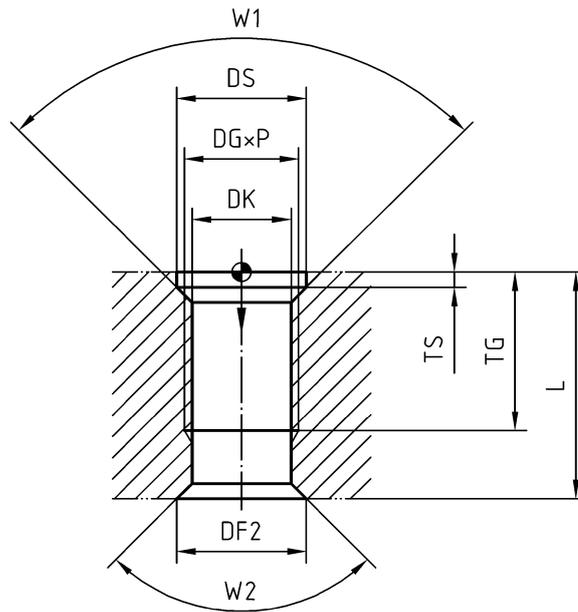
Gewindedurchgangsbohrung mit Schutzsenkung
